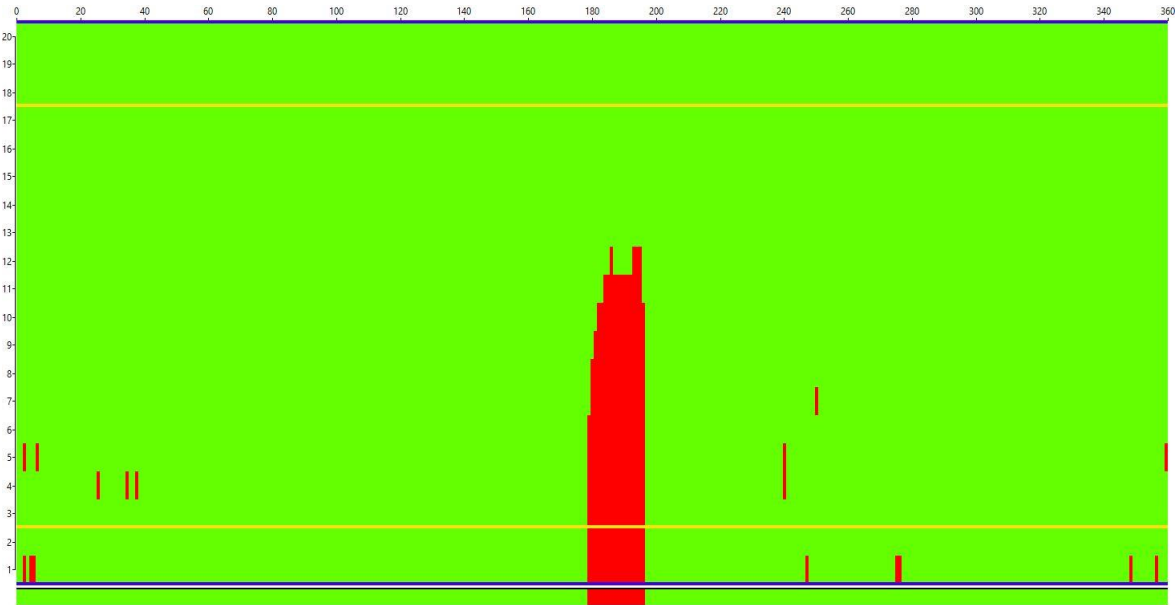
Cartografia típica de uma peça que revela um defeito de soldadura.
